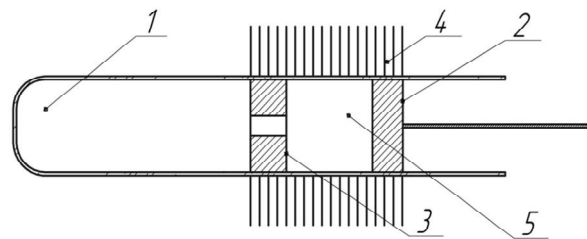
Свободнопоршневой двигатель без вытеснительного поршня – термообратимый двигатель:
